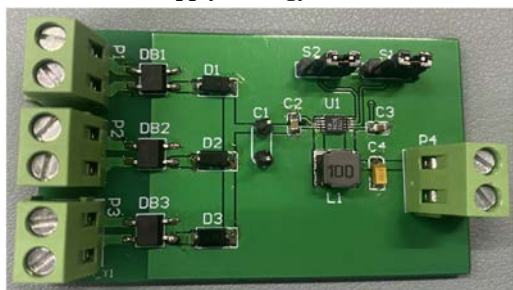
基于 LTC 3588-1 供电策略下的 PCB 实物图
